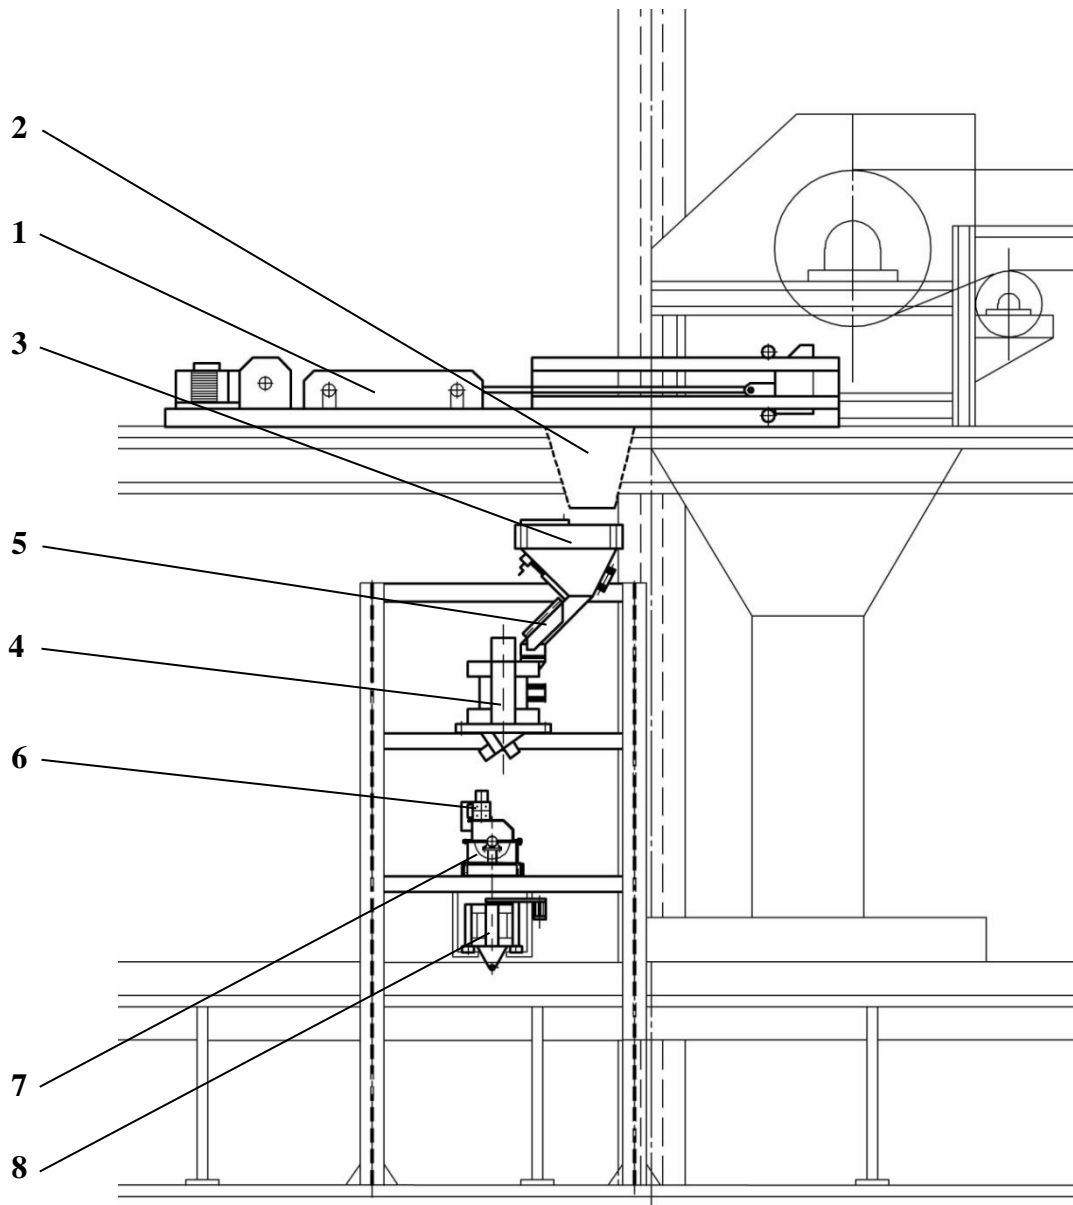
Аппаратная линия для отбора и подготовки проб дробленной сильвинитовой руды:
